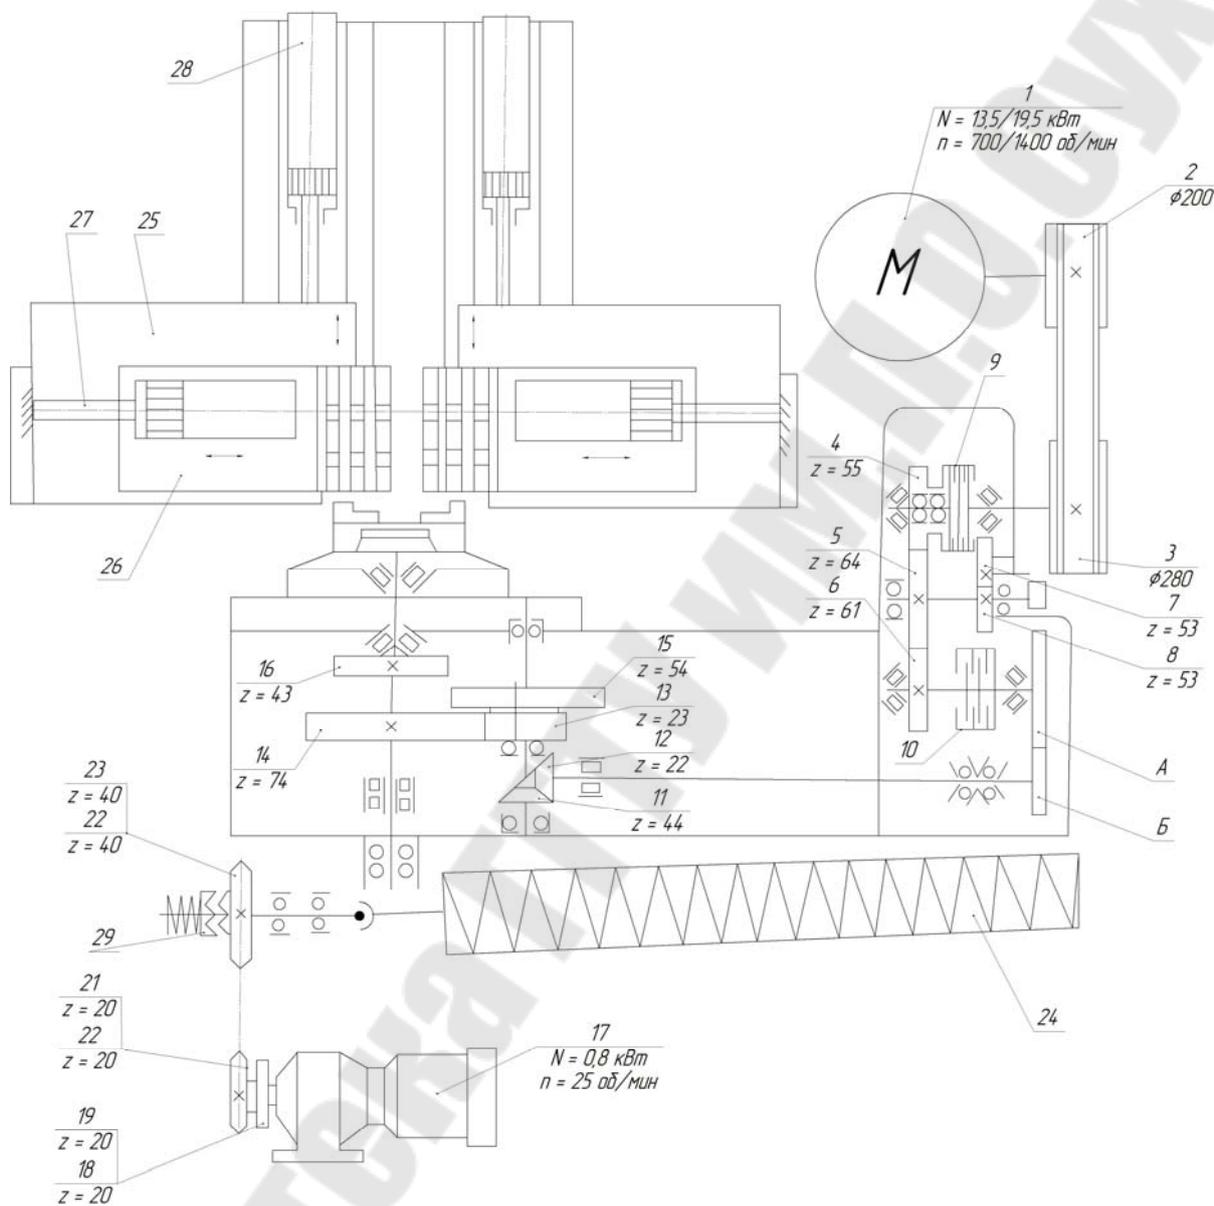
Кинематическая схема полуавтомата 1734: 1 – двигатель привода шпинделя; 2,3 – шкивы; 4 – 8, 11 – 26 – шестерни; 9 – 10, 26 – штифты; 17 – двигатель привода шнека, 18,19 – звездочки; 20 – шпиндель; 21 – каретка; 22 – цилиндр поперечного перемещения; 23 – суппорт поперечный; 24 – шнек; 25 – цилиндр продольного перемещения
